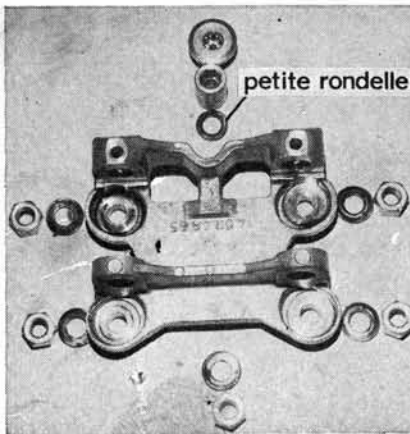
Les six fixations de culasse (Photo RMT)
